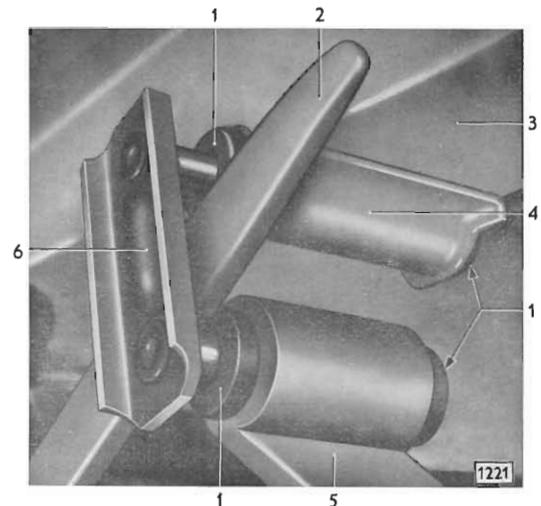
An der rechten hinteren Federaufhängung Lasche mit Gehängebolzen aus Aufnahme im Rahmenlängsträger und aus Federauge herauszwingen
